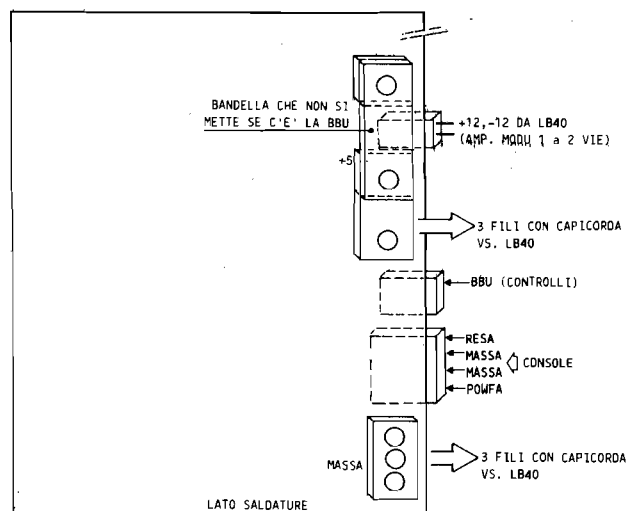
Vista posteriore del BACK PLANE e dei suoi connettori
